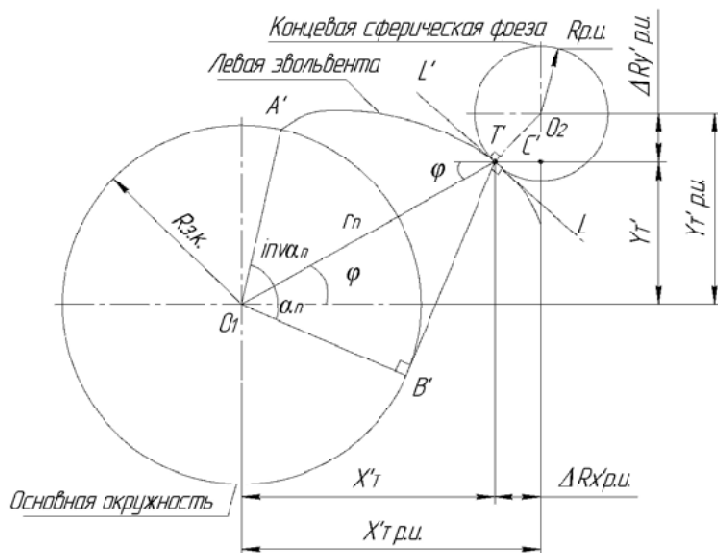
Расположение концевой фрезы на левой эвольвенте (вид в плане)
